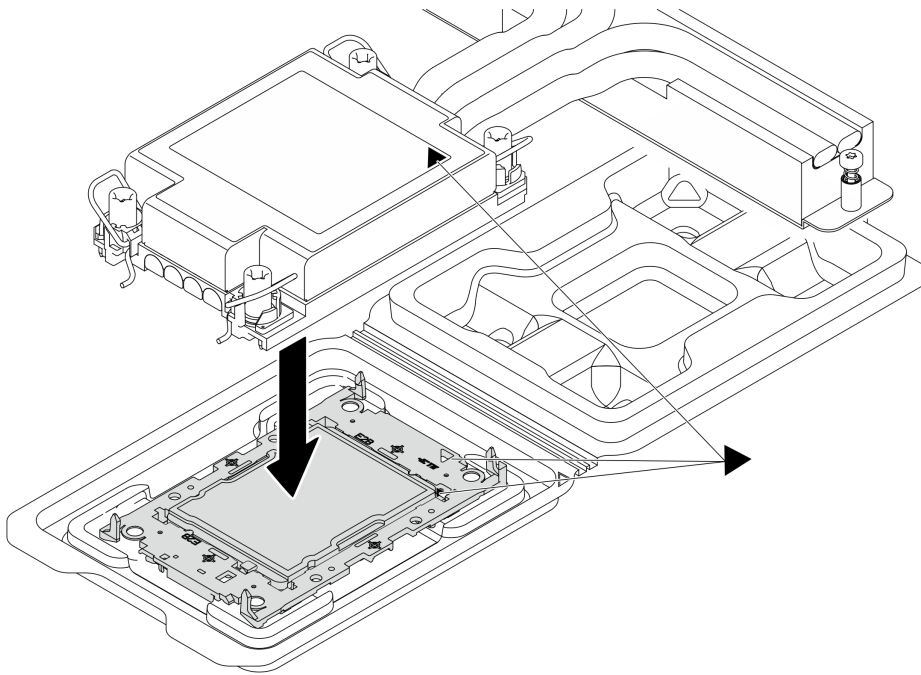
Assemblage du module de processeur et dissipateur thermique avec le processeur dans le plateau d'expédition
